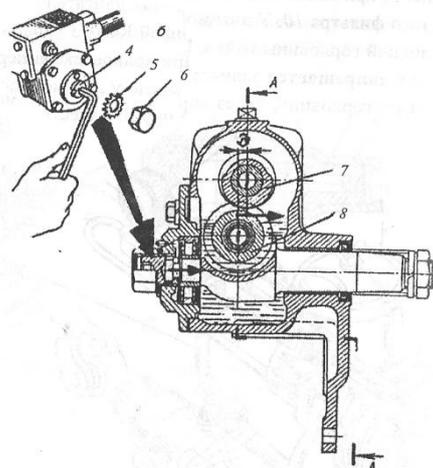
Регулировка рулевого механизма ГАЗ-53А:
